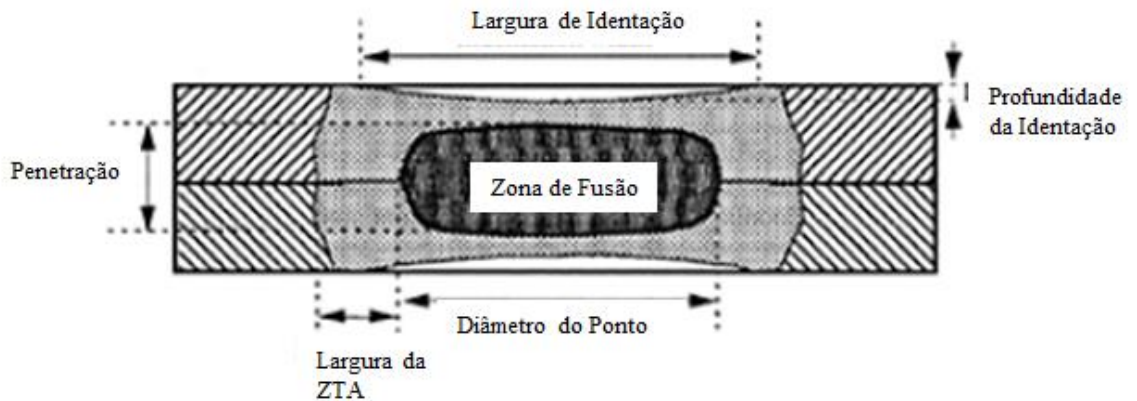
Características Geométricas do Ponto de Solda
